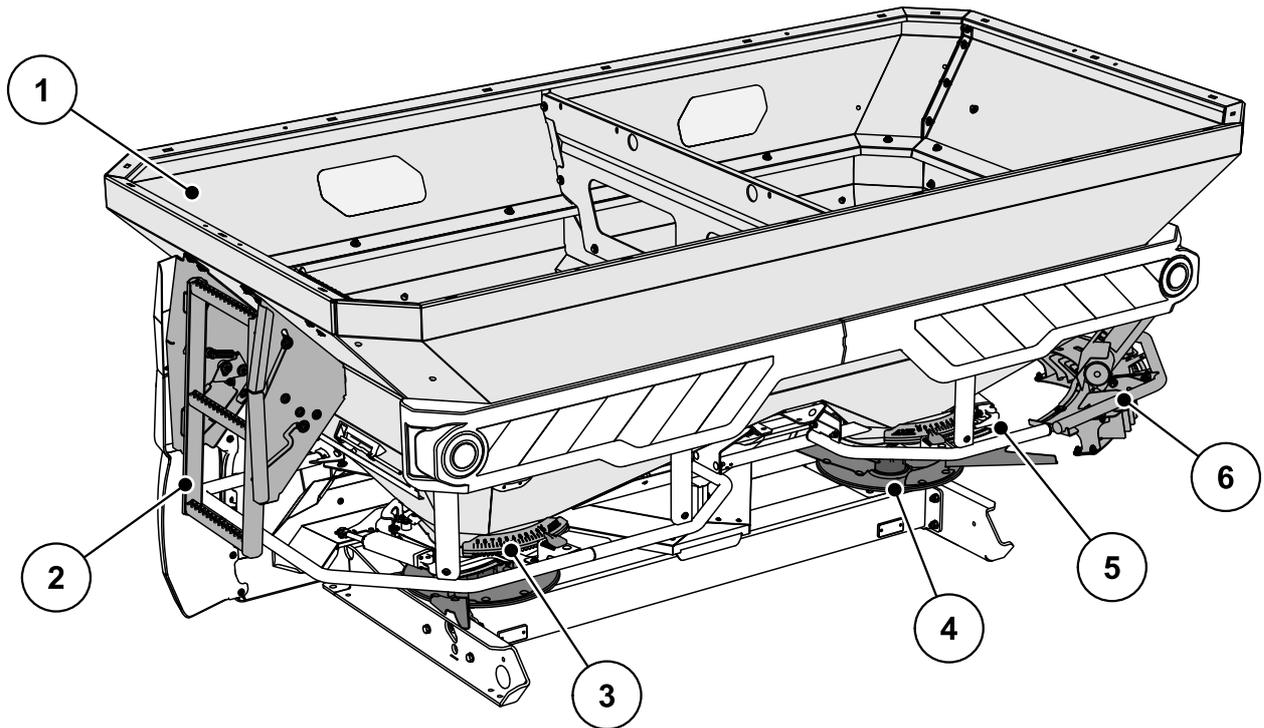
Aperçu des composants AXIS 50.2 - vue arrière
